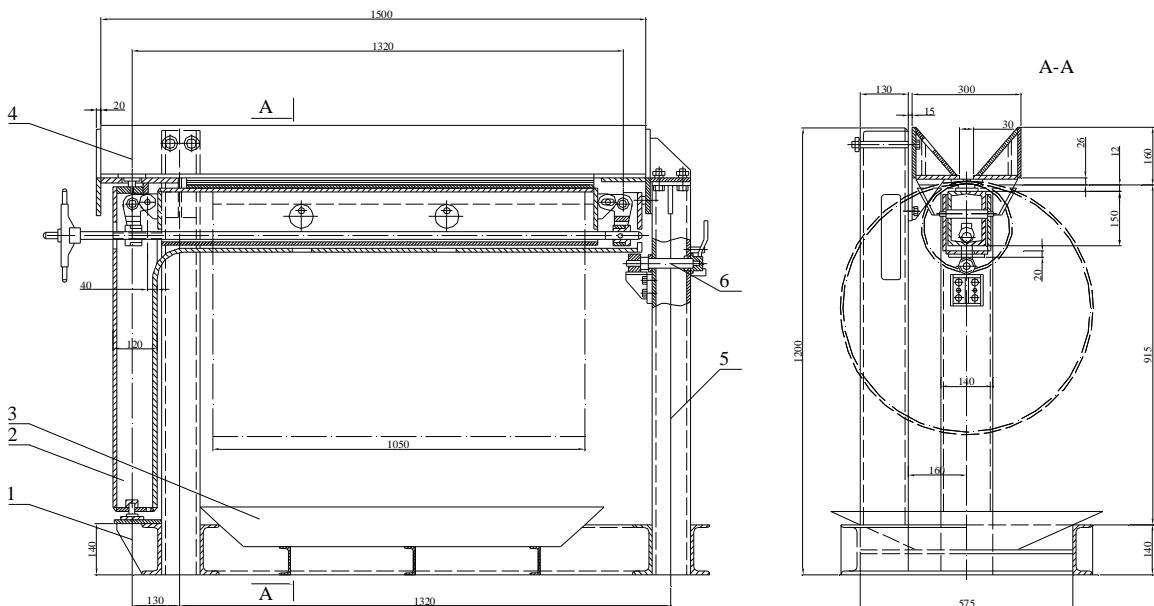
Установка для сварки продольного шва обечайки.
